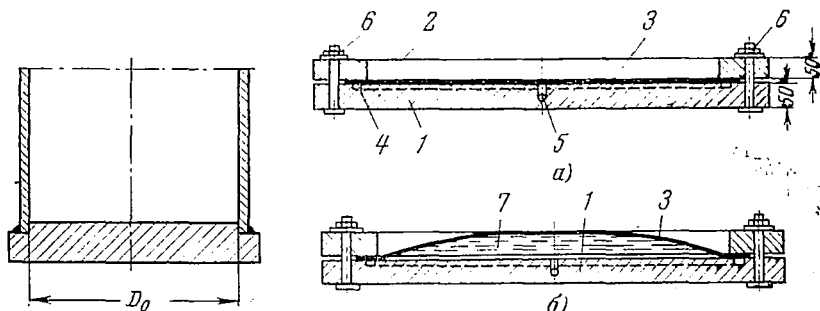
Вварка плоского толстого днища в обечайку электродуговой сваркой.
